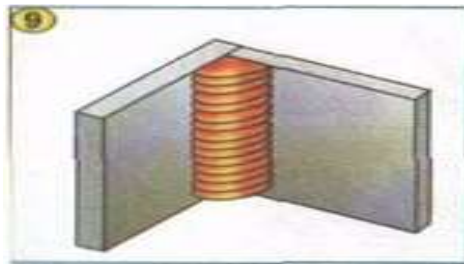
Сварка углового и таврового соединений.
